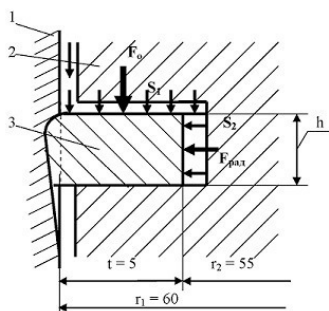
Газодинамическая схема работы компрессионного кольца двигателя КАМАЗ
